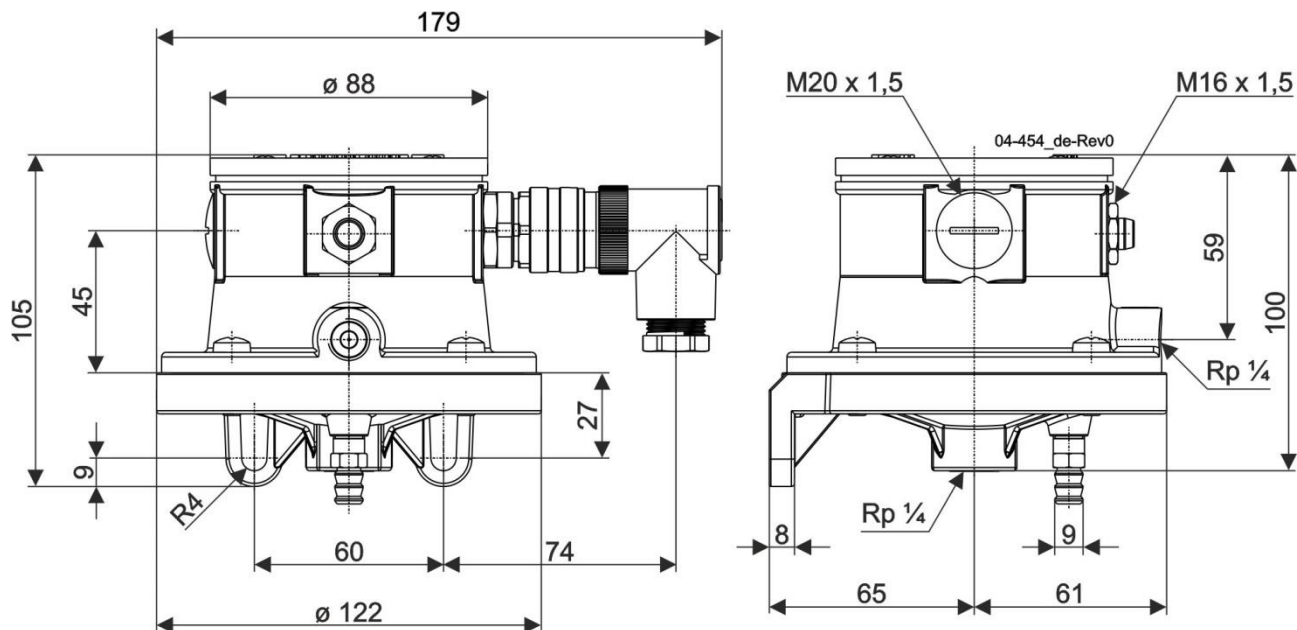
Maßblatt Druckwächter (Ausführung mit Signallampe und Gerätestecker 4 + PE)
